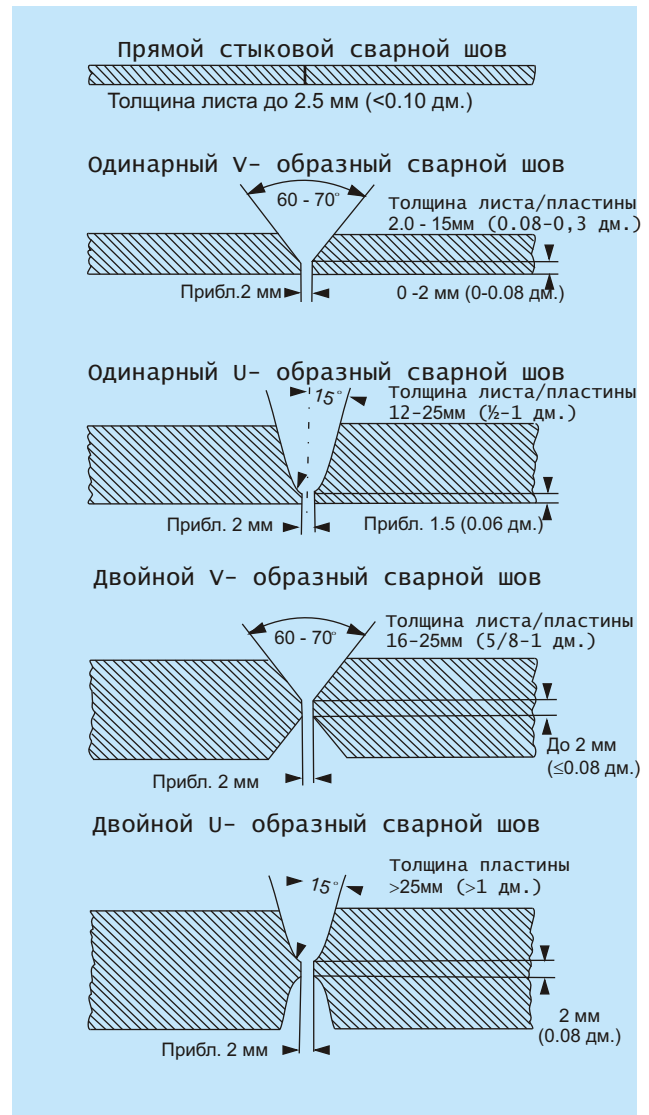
Подготовка кромок для сваривания никелевых сплавов и специальной нержавеющей стали
